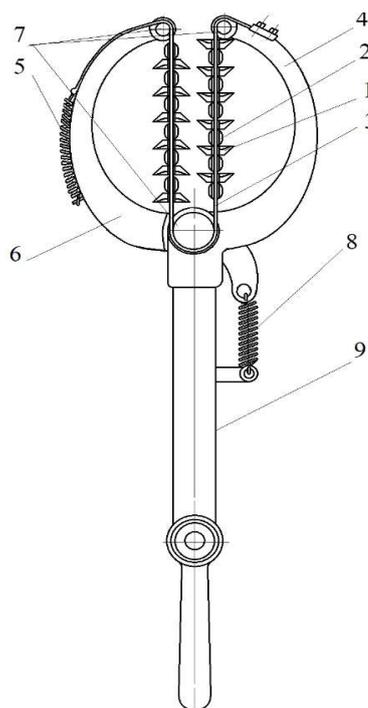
Пружинящее устройство для кольцевания деревьев: 1 – режущий орган, 2 – цилиндрические вставки, 3 – гибкий канат, 4 – неподвижный зажимной рычаг, 5 – натяжная пружина, 6 – подвижный зажимной рычаг, 7 – блок, 8 – прижимная пружина, 9 – рукоятка
